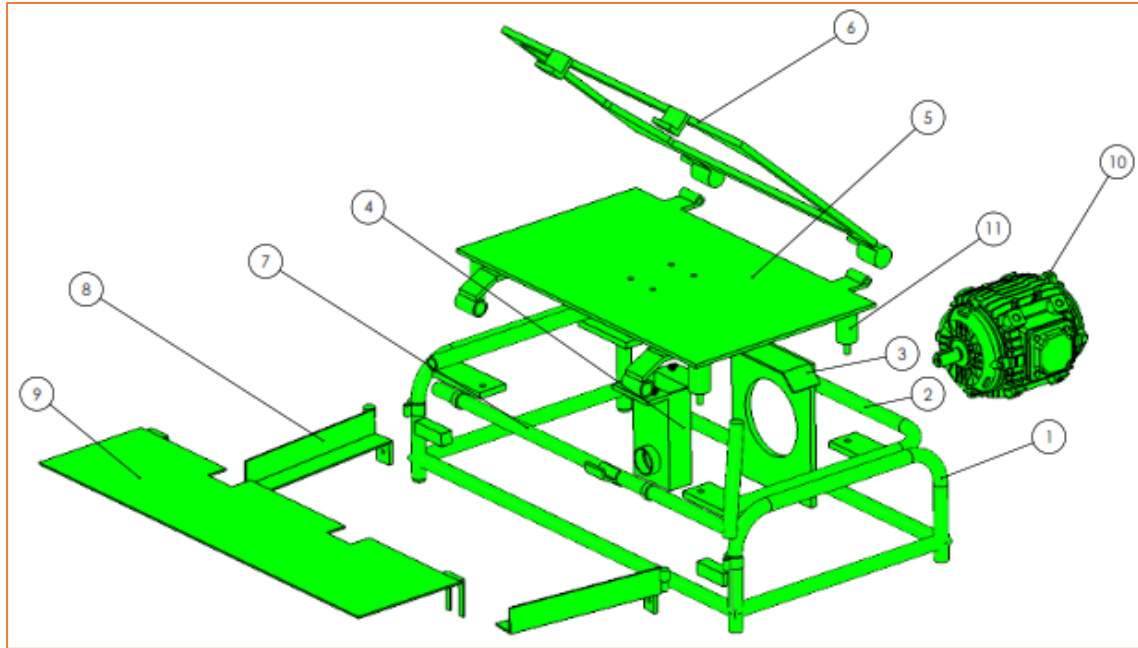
Despiece de la máquina TEVI de la fundación EcoSur.
